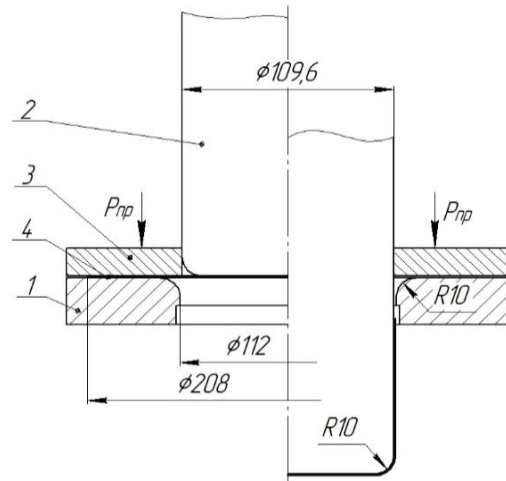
Схема першої витяжки: 1 – матриця, 2 – пуансон, 3 – притискач, 4 – заготовка
